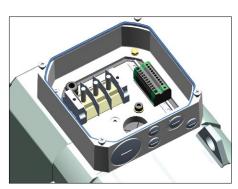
Plaque à bornes pour tailles de moteur 100 - 160
